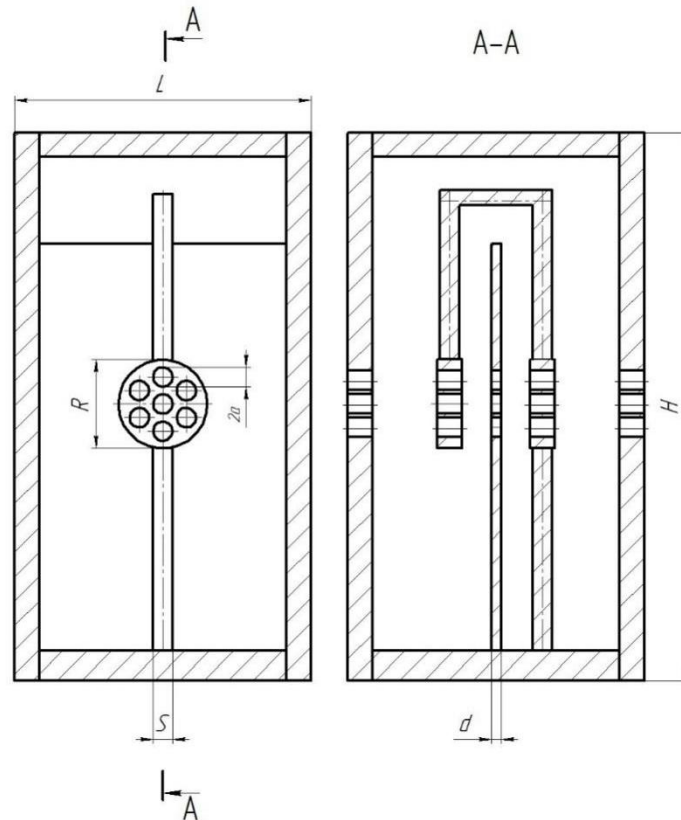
Эскиз четырехзворного прямоугольного резонатора
